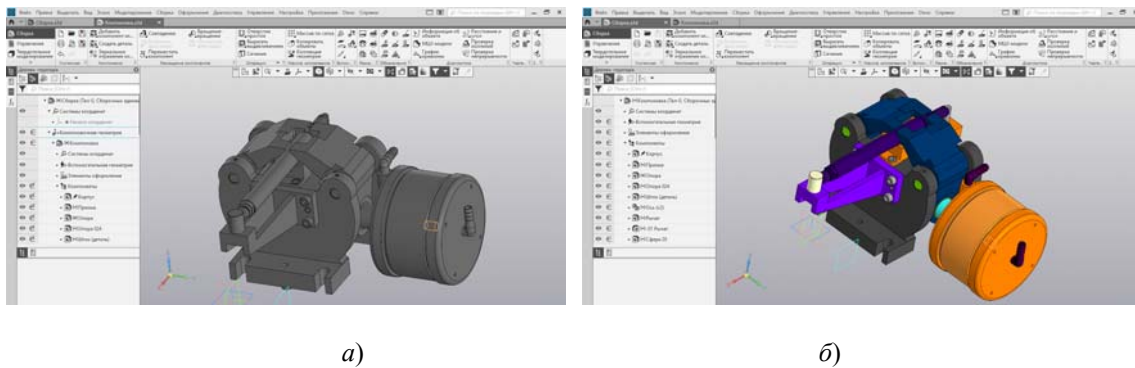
Компоновочная геометрия (а) и сборочная 3D-модель станочного приспособления, выполненная на основе компоновочной геометрии (б)
